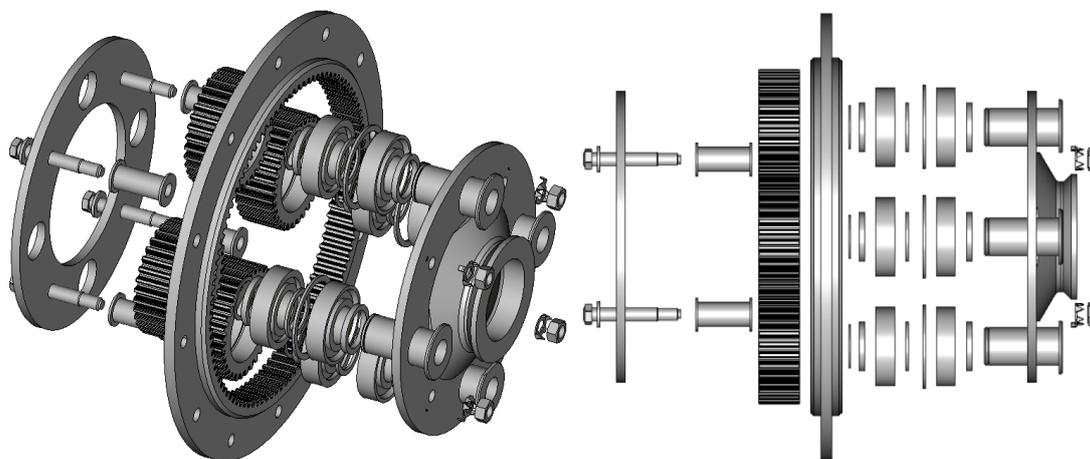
Состав сборки планетарной передачи (слева – направо):
